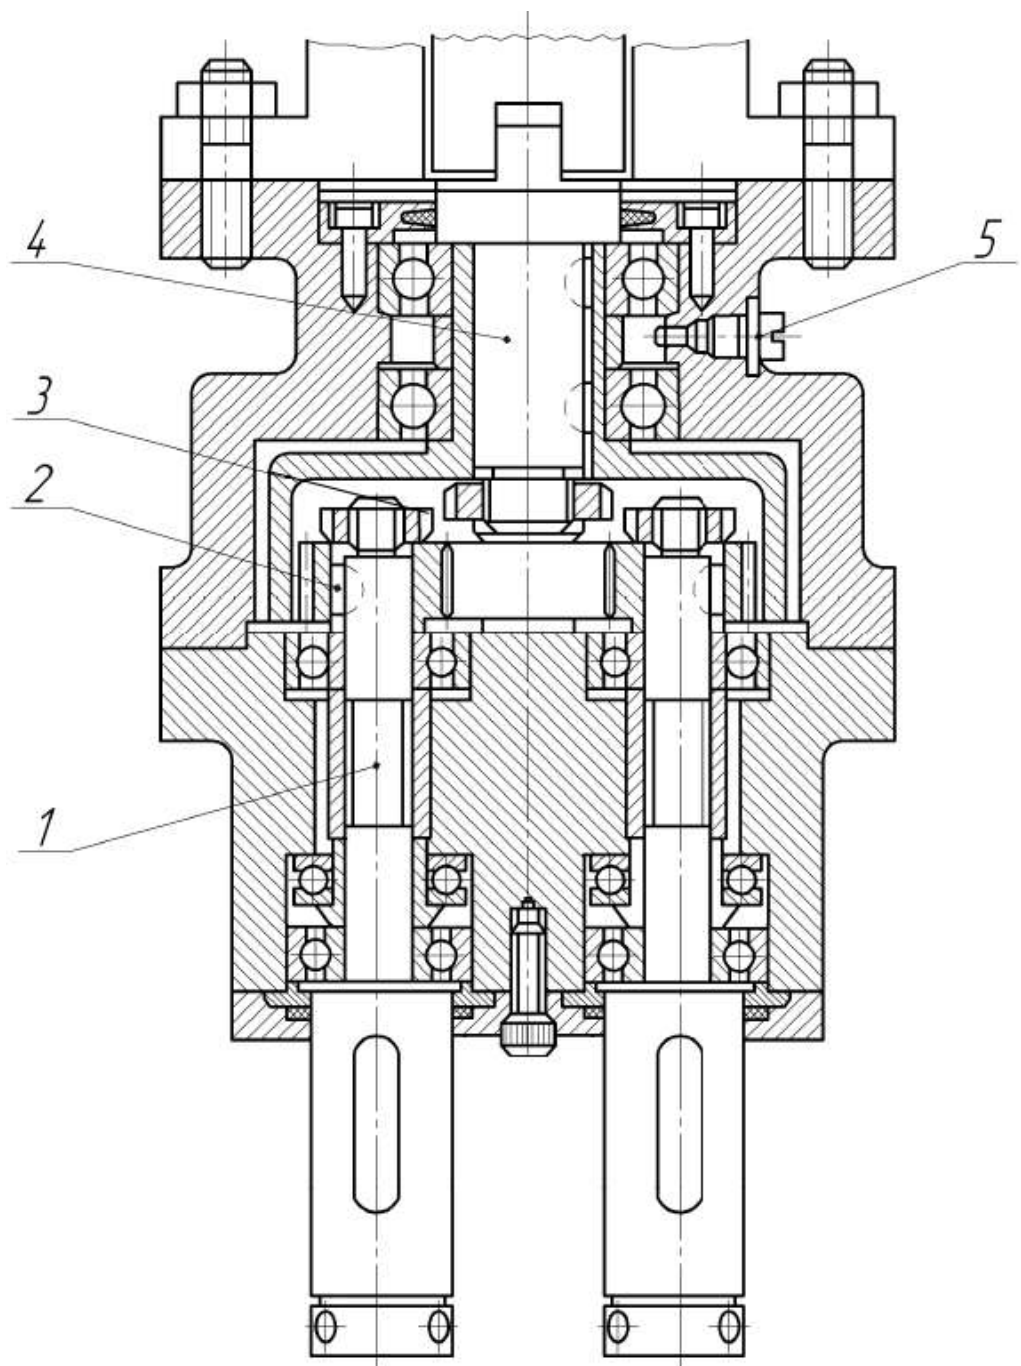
Конструкція двошпindelної свердлильної головки
